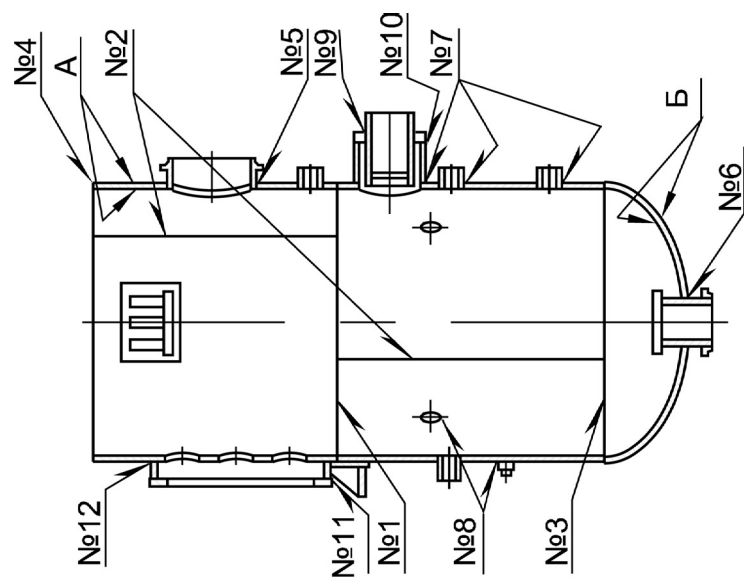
Сварные швы корпуса ПНД:
